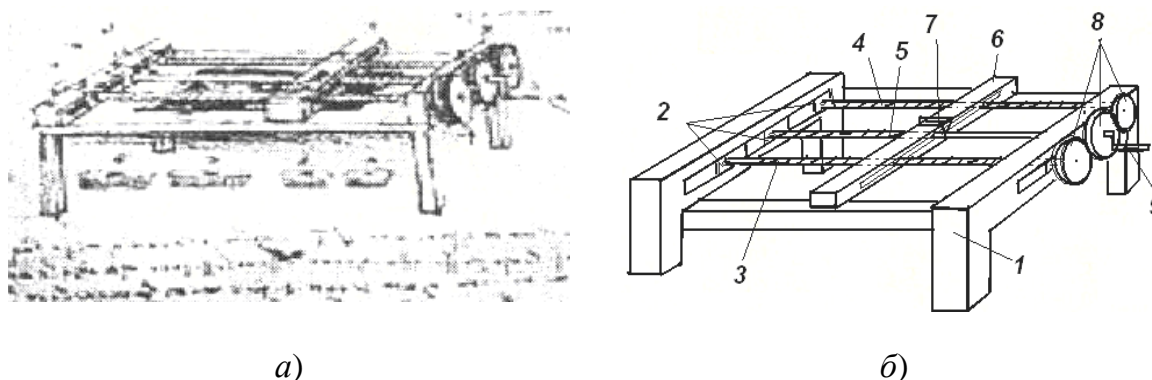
Рисунок токарно-винторезного станка Леонардо да Винчи:
